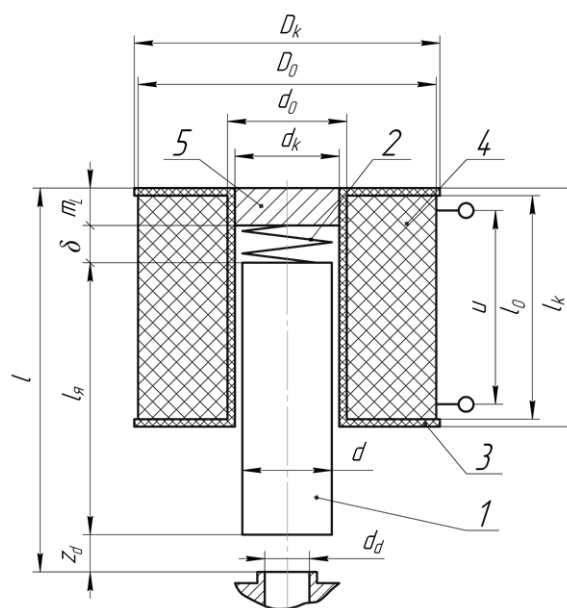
Схема электромагнитного дозатора газа: 1 – клапан-сердечник перепуска газа; 2 – предварительно сжатая пружина; 3 – корпус катушки; 4 – обмотка катушки; 5 – упор; D_k и d_k – наружный и внутренний диаметры электромагнитной катушки; l_k – длина корпуса катушки
